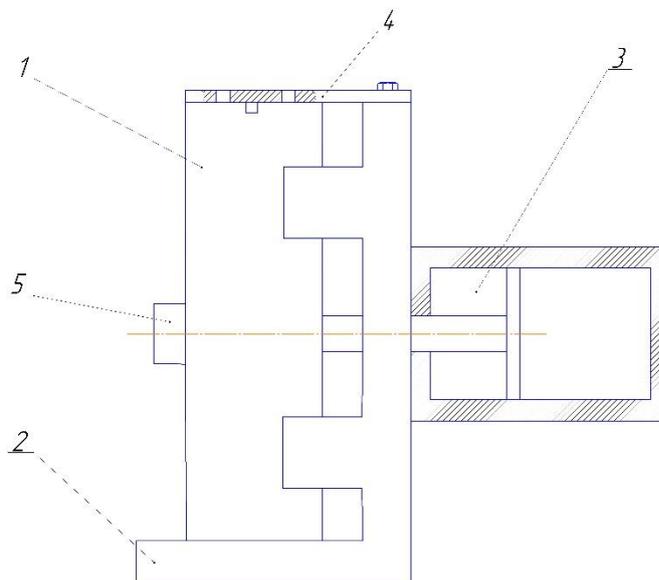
Кинематическая схема пневматического зажима с кондуктором
